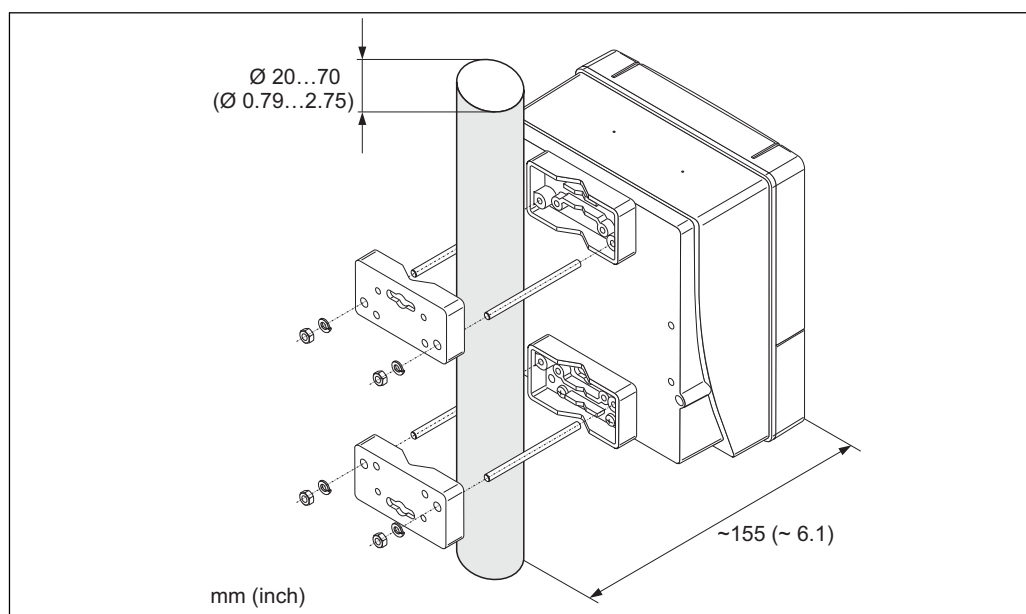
Montage sur conduite (boîtier pour montage mural)
